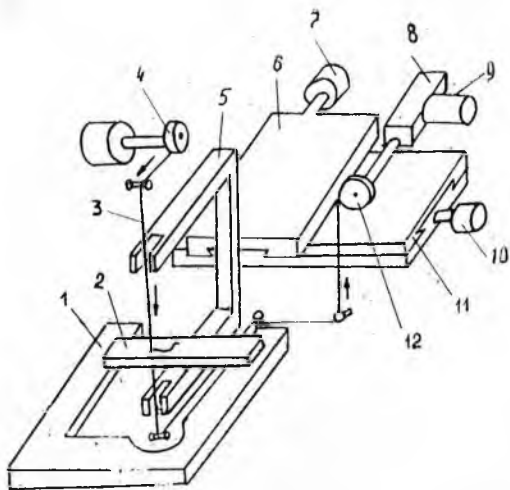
Схема электроимпульсной обработки способом вырезания электродом-проволокой: 1 — стол; 2 — заготовка; 3 — электрод-проволока; 4, 12 — барабаны; 5 — скоба; 6, 11 — суппорты; 7, 10 — автоматические регуляторы подачи; 8 — редуктор; 9 — электродвигатель
